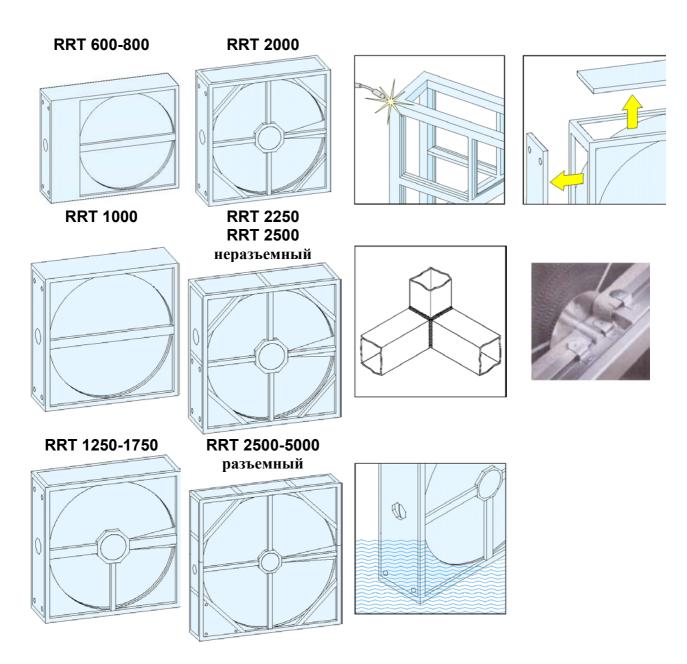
Корпус регенеративного теплоутилизатора с алюминиевой рамой
